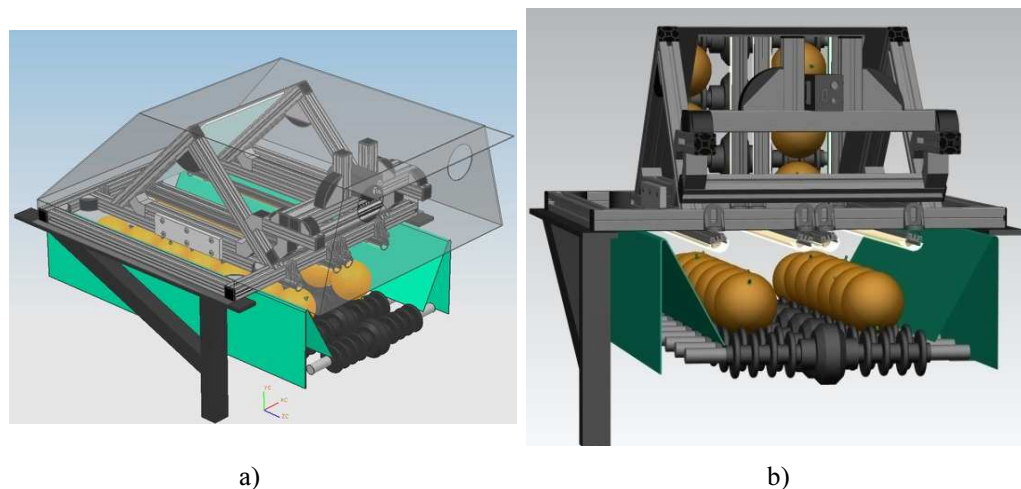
a) Diseño completo de la zona de inspección; b) Interior de la zona de inspección
